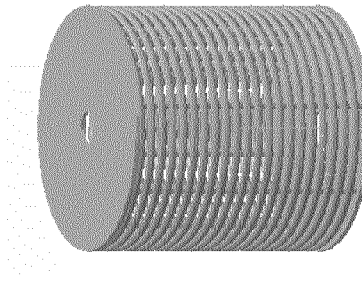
Циліндричний барабан з прутковою поверхнею
